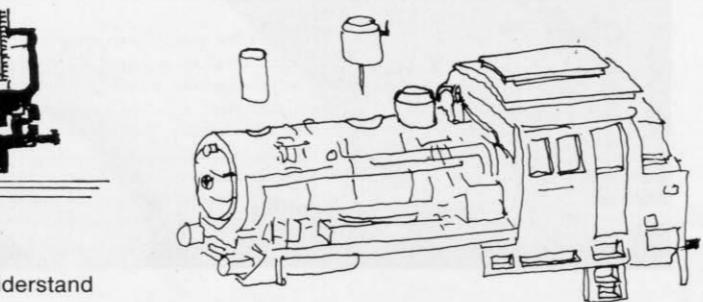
Explosionszeichnung mit den einzelnen Bauteilen.
